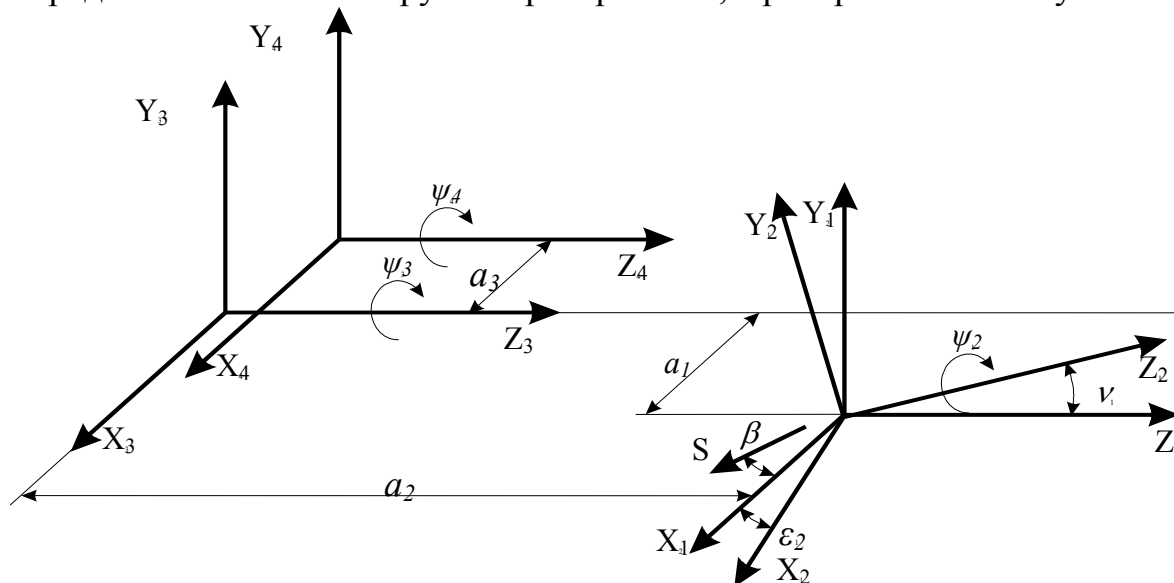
Обобщенная система реперов при шлифовании заготовки
